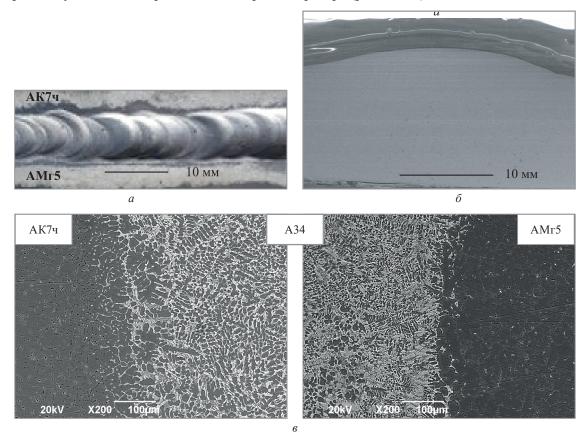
Сварной шов АК7ч—АМг5, сформированный припоем А34 в качестве присадочного материала: a — сварной шов; δ — макроструктура сварного шва; ϵ — микроструктура сварного шва
